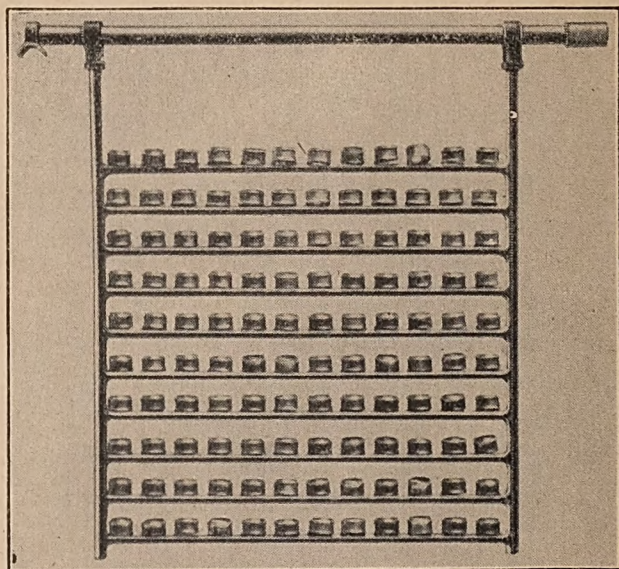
Montage sur lequel sont fixées 120 pièces.
